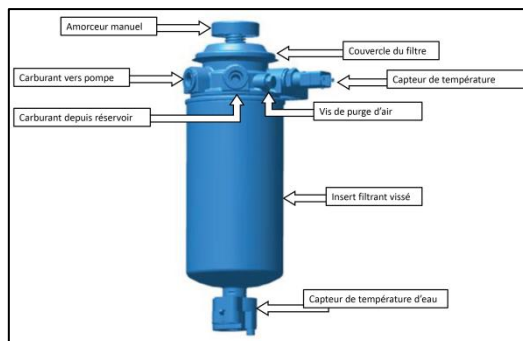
PURGE D' AIR DU FILTRE À CARBURANT
